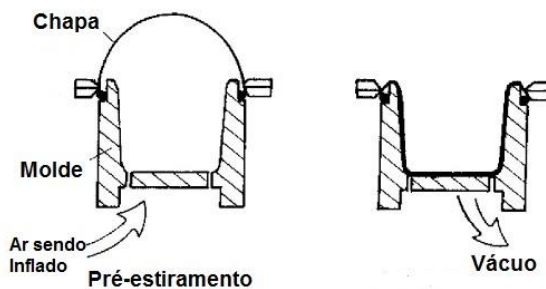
Desenho esquemático exemplificando a moldagem por sopro auxiliada por vácuo.
